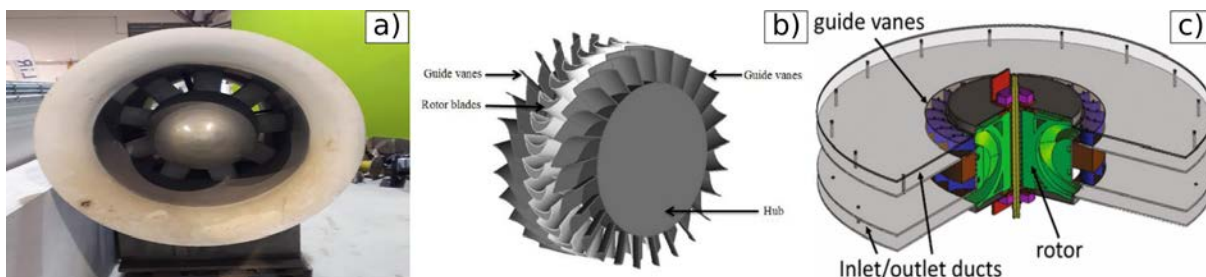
a) Turbina Wells. b) Turbina de impulso [4]. c) Turbina biradial [5].
